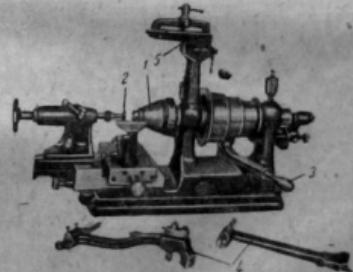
Револьверный станок Бреге для обточки корпусов.
